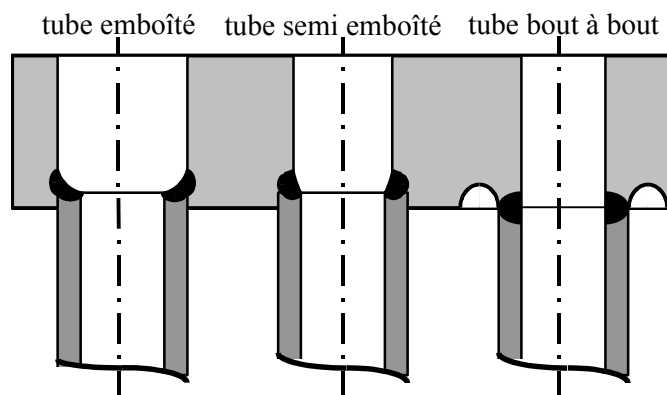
Assemblage tube sur plaque intérieur tube
